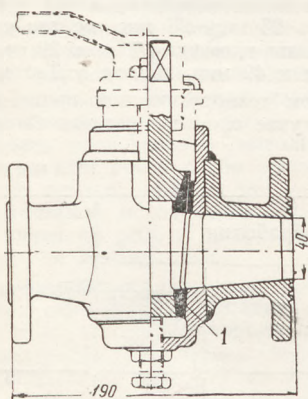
Биметаллический разобцительный клапан: 1 — сварное гнездо
